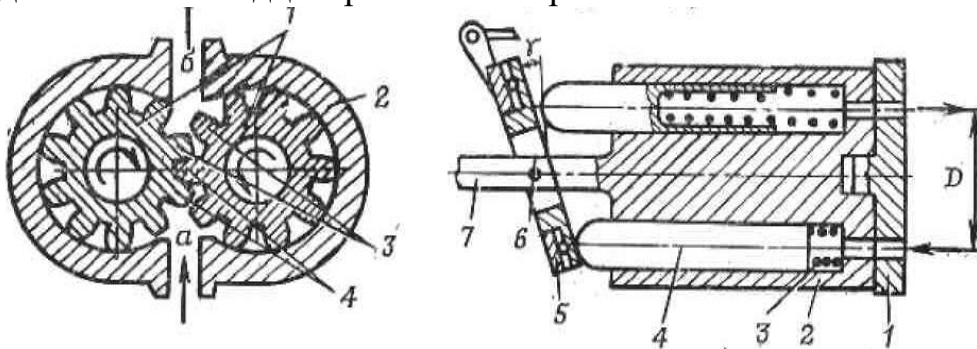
Схема шестеренного насоса: а - порожнина всмоктування; б - порожнина нагнітання; 1 - шестерні; 2 - корпус; 3, 4 - зуби шестерень
